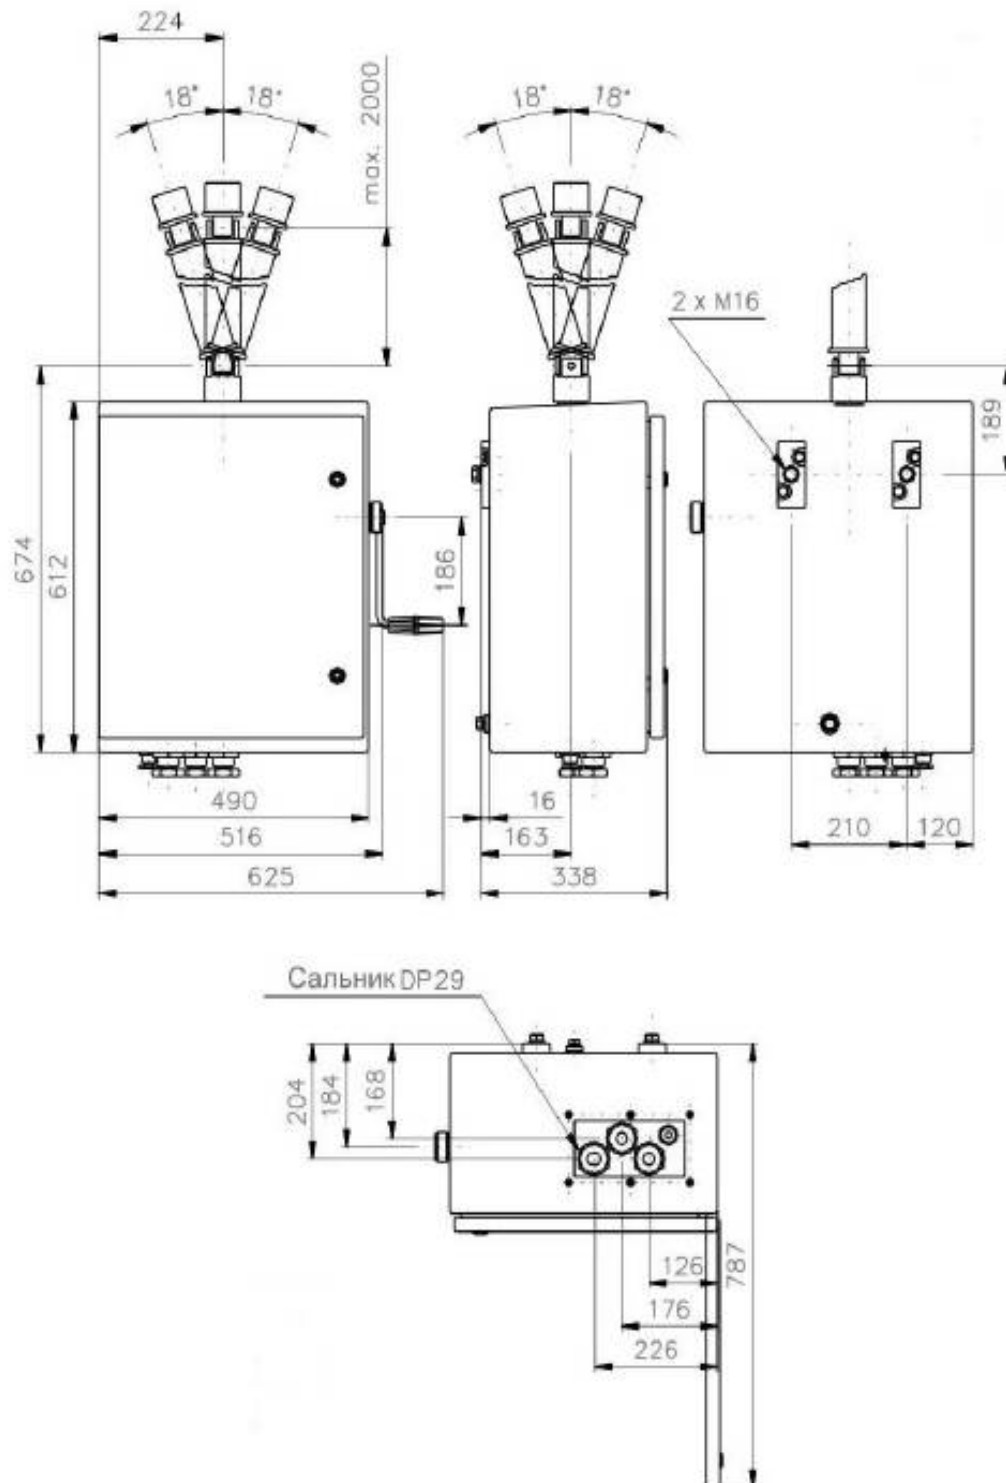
Габаритно-присоединительные размеры электродвигательного привода разъединителей серии РГП-НТ-35
